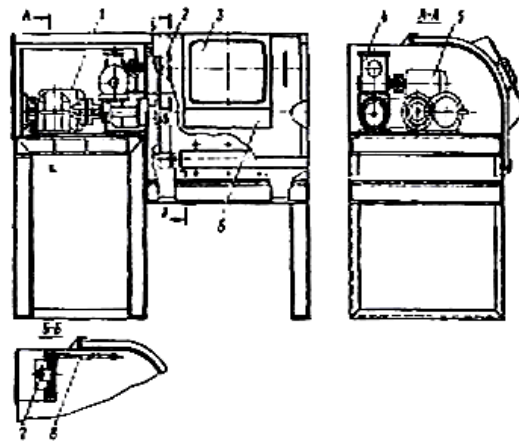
Верстат СПМ-1 для плазмової металізації чавунних корпусних деталей автомобіля.
